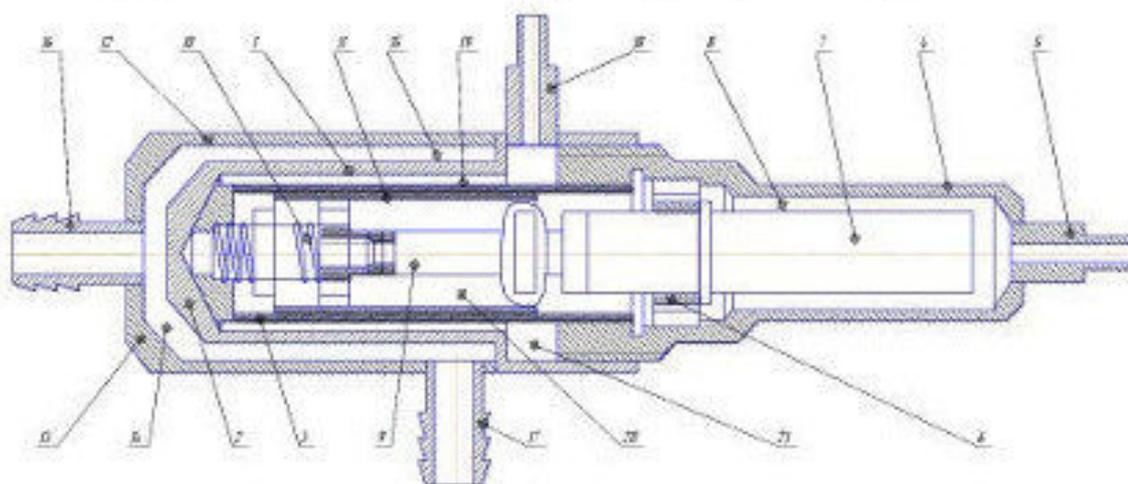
Саморегулирующийся подогреватель топлива
